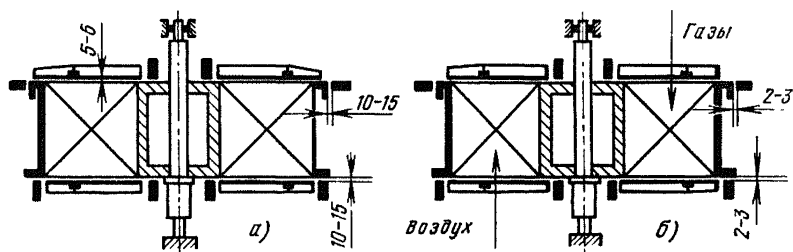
Регулировка уплотнений РВП с опертым ротором.
